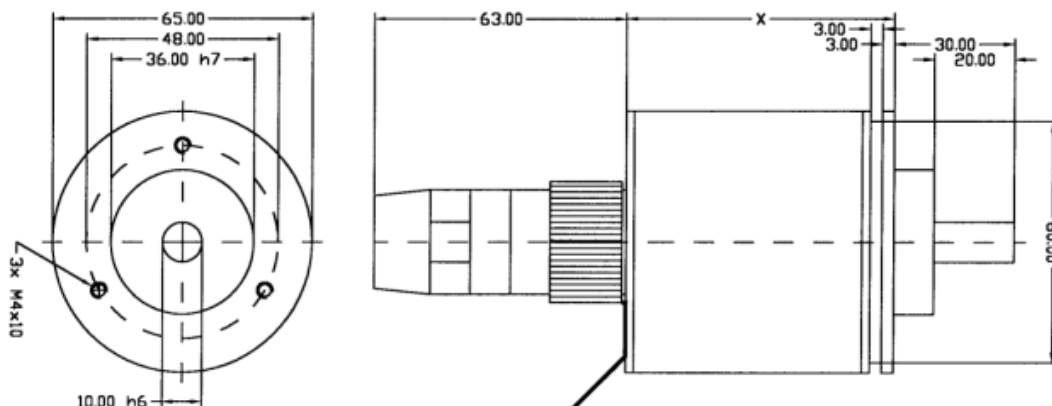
Maßzeichnung ROTARNOCK RS232 oder RS485, Option IF, Ausführung IP65
